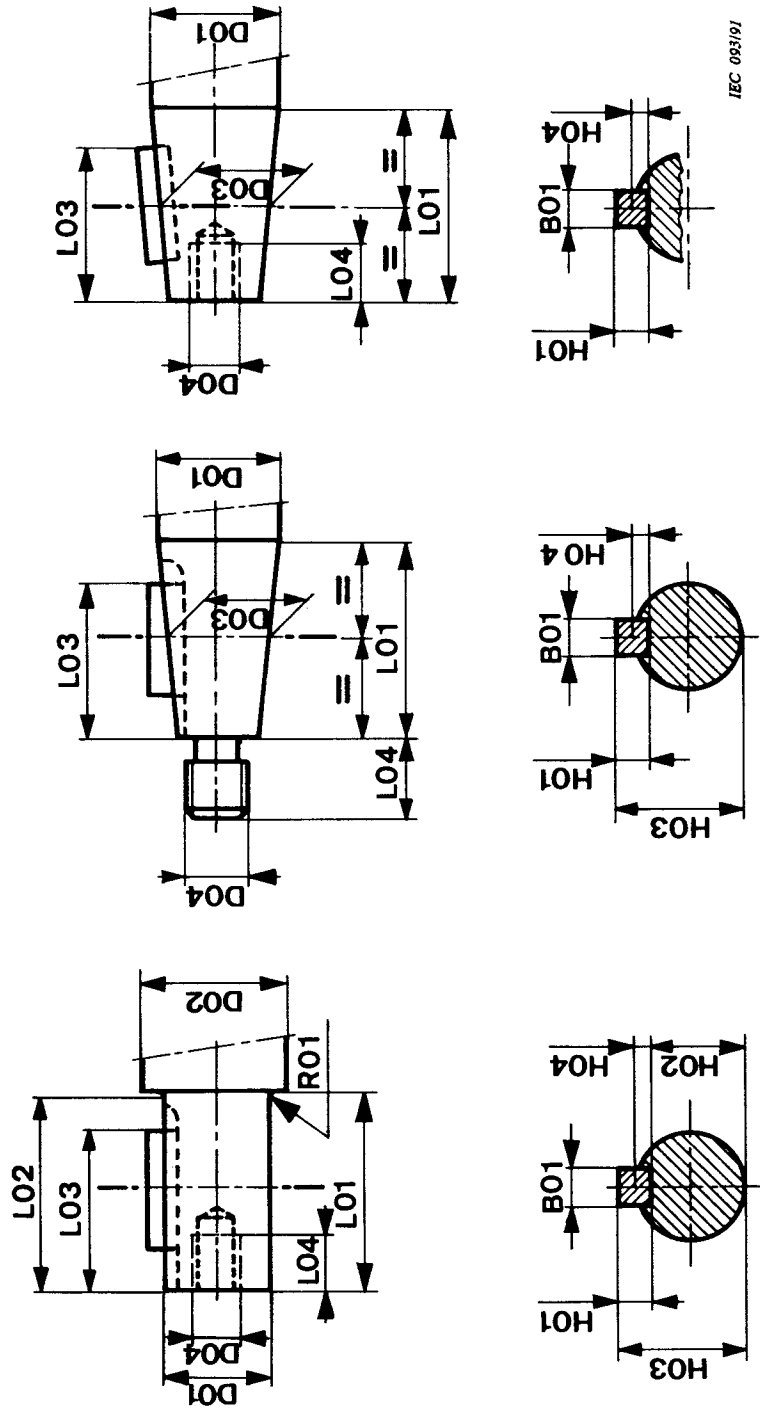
Dimensions de montage de l'arbre côté D de la machine
